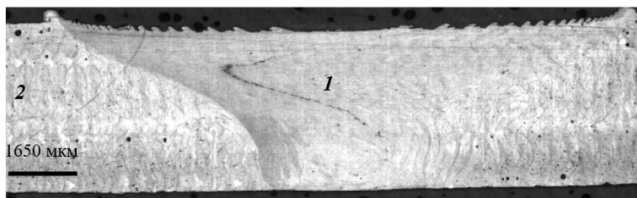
Панорама сварного соединения пластин сплава АК9, выполненного сваркой трением с перемешиванием (СТП):
